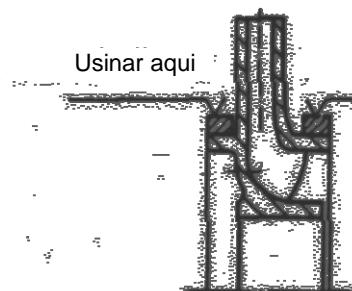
Usinado o diâmetro externo do anel de desgaste do rotor.
